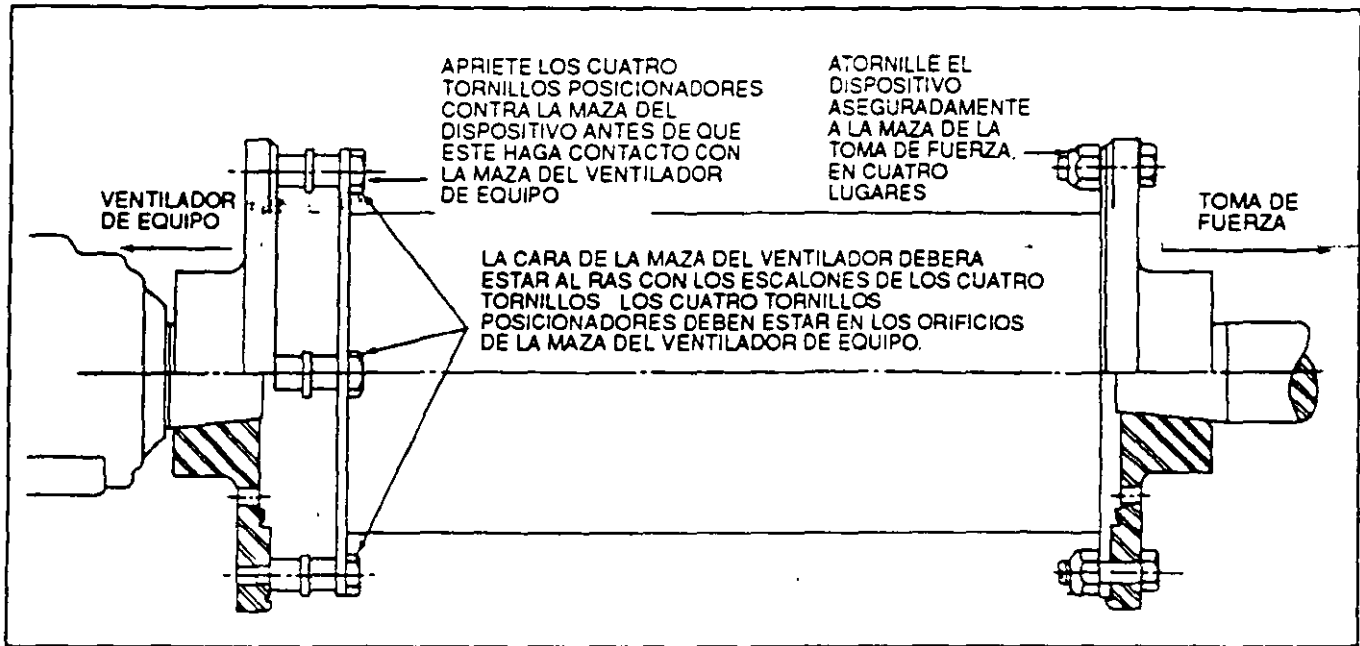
DISPOSITIVO MONTADO A LA MAZA DE LA TOMA DE FUERZA. E-27092A-S
